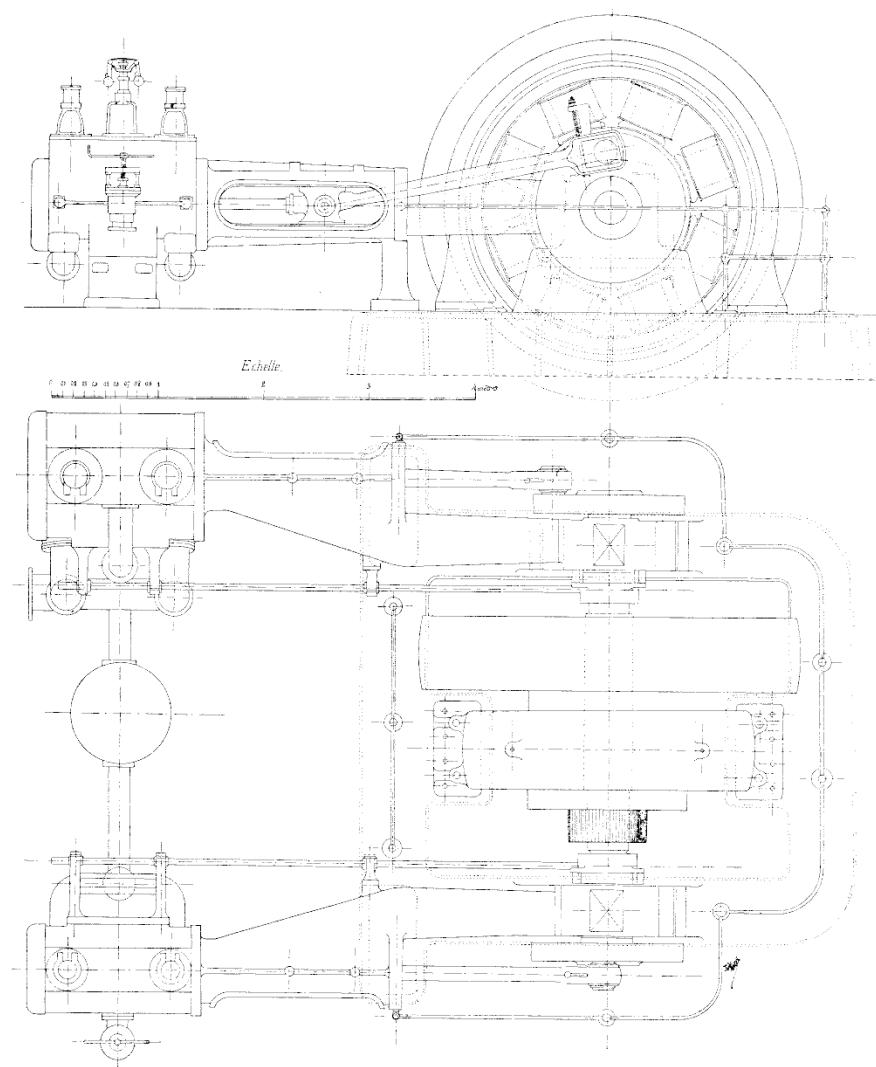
Dynamo Scott et Mountain. — Details de construction.
